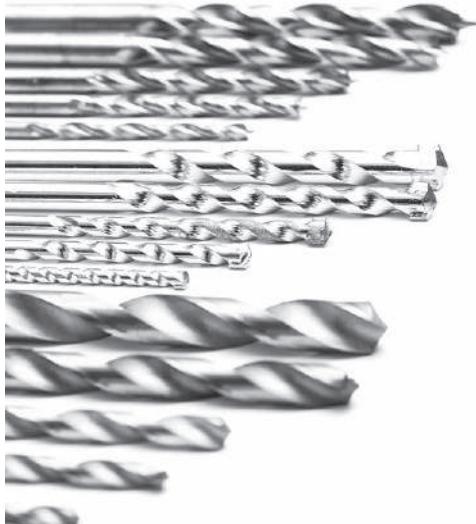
Сверху вниз — сверла по дереву, буры, сверла по металлу
